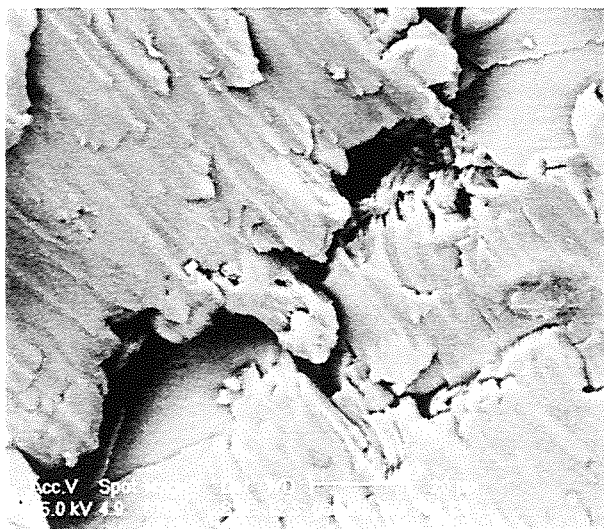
Detalle de una fisura detectada en la superficie de fractura
